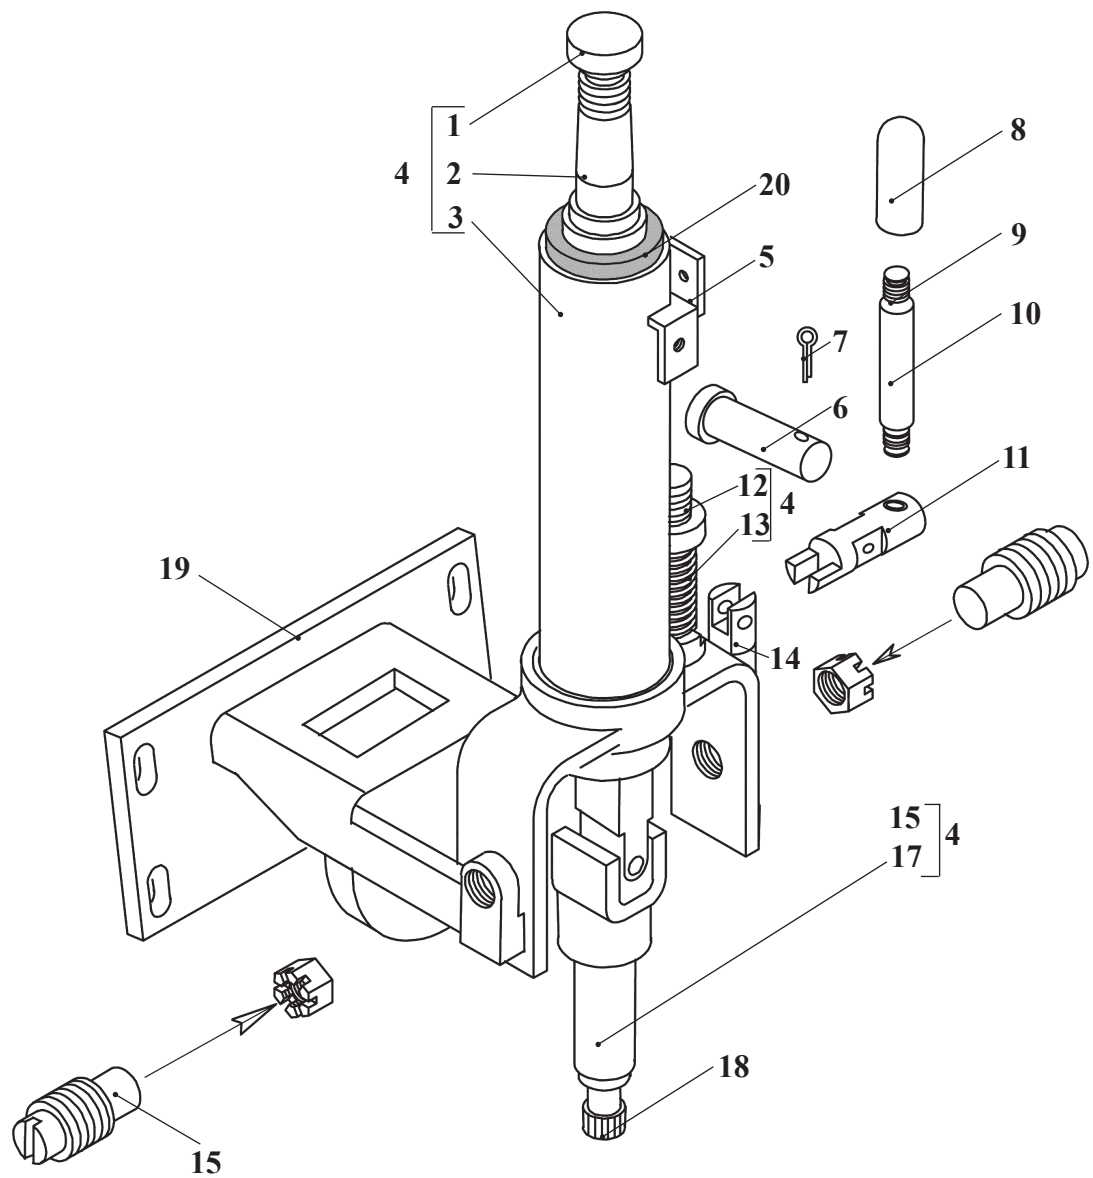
У7810.7-9.02.01.750-01	Привод руля
